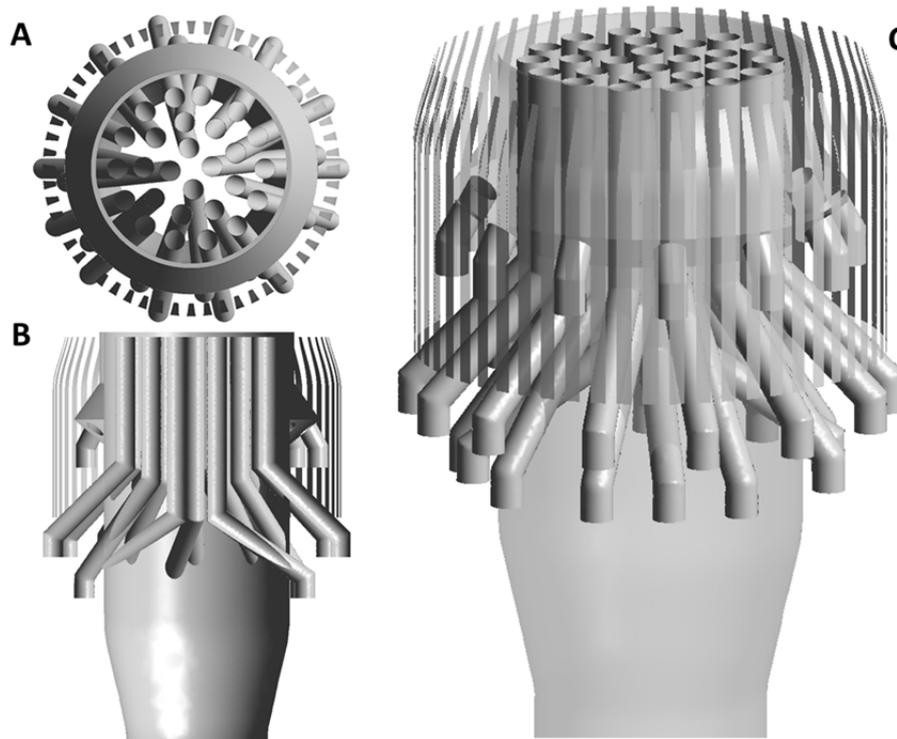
Sketch del terminale RV-101-C: (A) vista in pianta; (B) sezione frontale; (C) vista tridimensionale.
